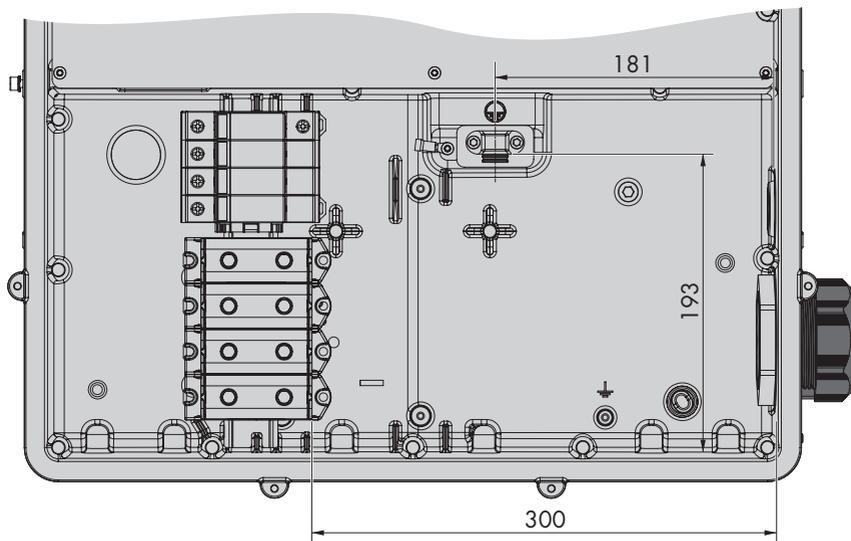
Vista interior da Connection Unit CA com dimensões para os condutores (dimensões em mm)
